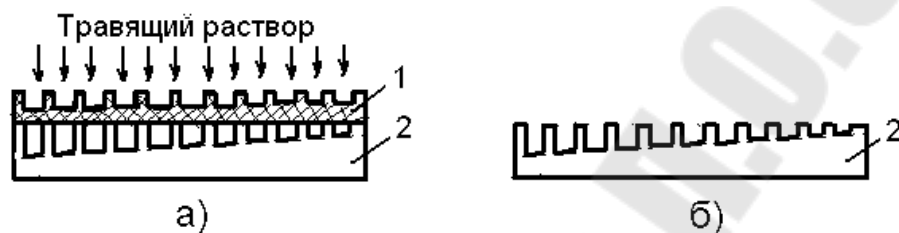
Схема изготовления формы глубокой печати пигментным способом
